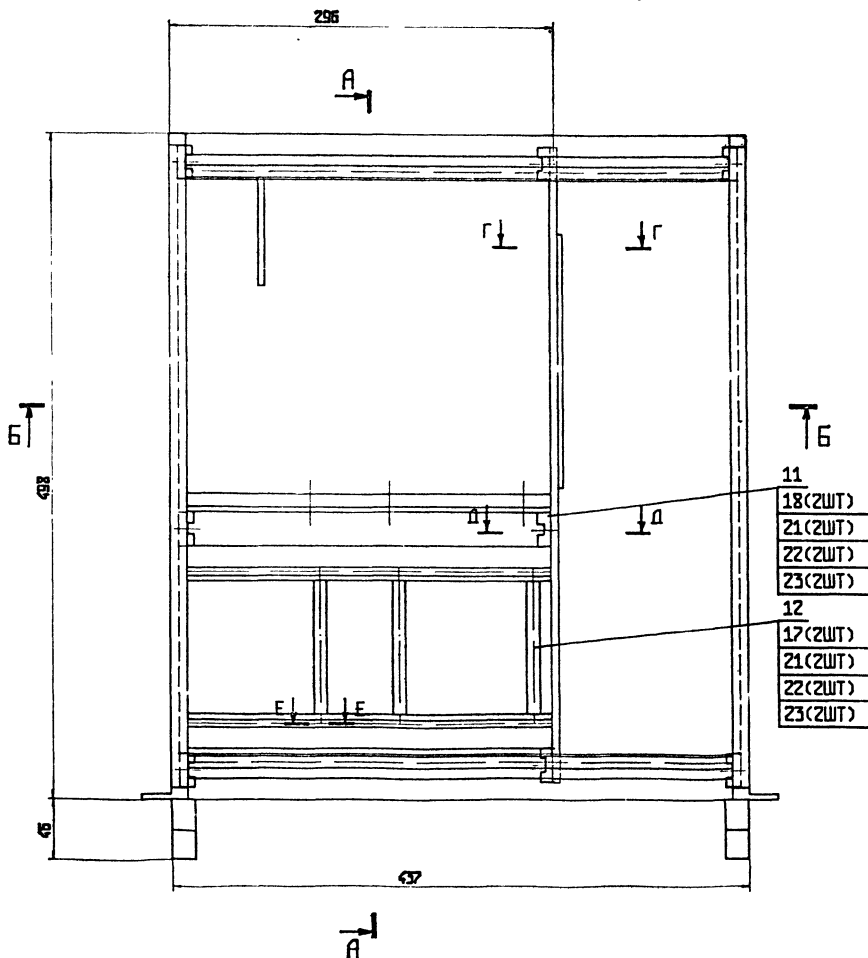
Фрагмент сборочного чертежа корпуса для информационной базы 258
